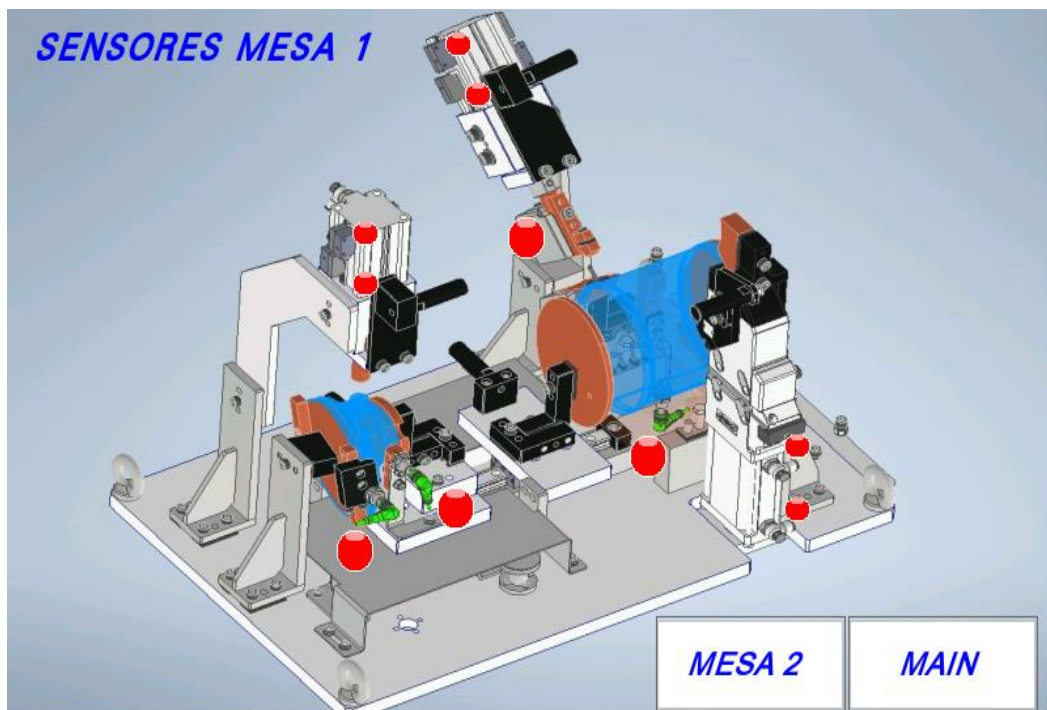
Layout con indicadores de sensores. Fuente. elaboración propia
